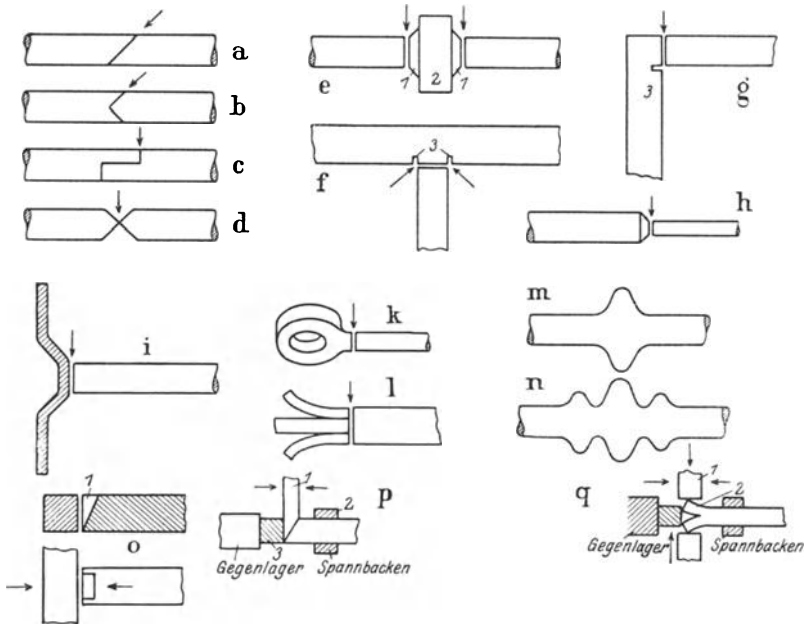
Vorbereitungsarbeiten bei Stumpfschweißungen.
